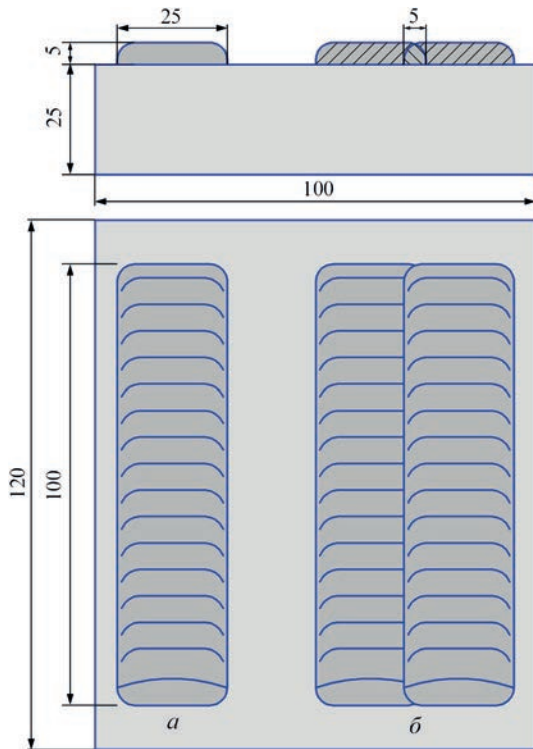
Схема наплавлення пластин для дослідження формування і стійкості наплавленого металу проти тріщин: а – одиничний валик; б – подвійний валик з перекриттям
